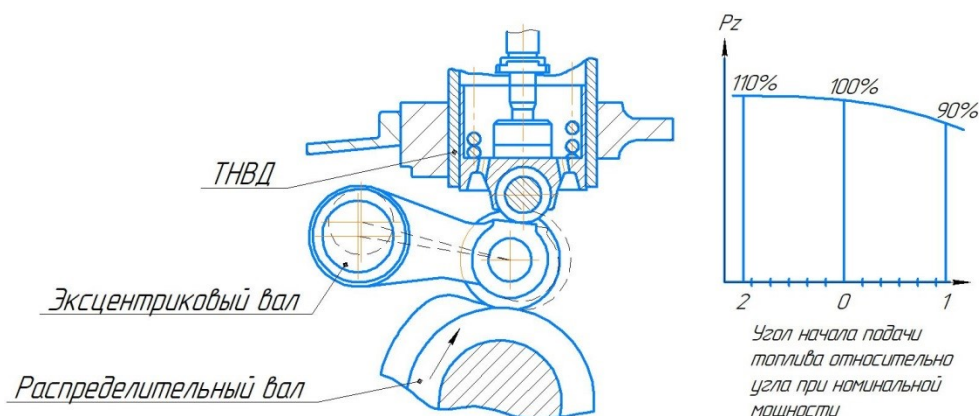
Рычажный механизм регулировки начала подачи топлива.
